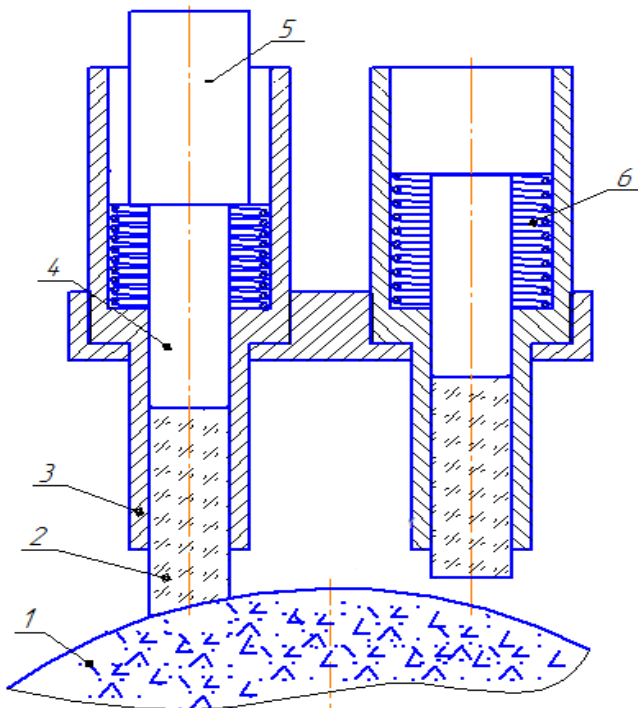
Приспособление для подачи СОЖ в зону обработки
